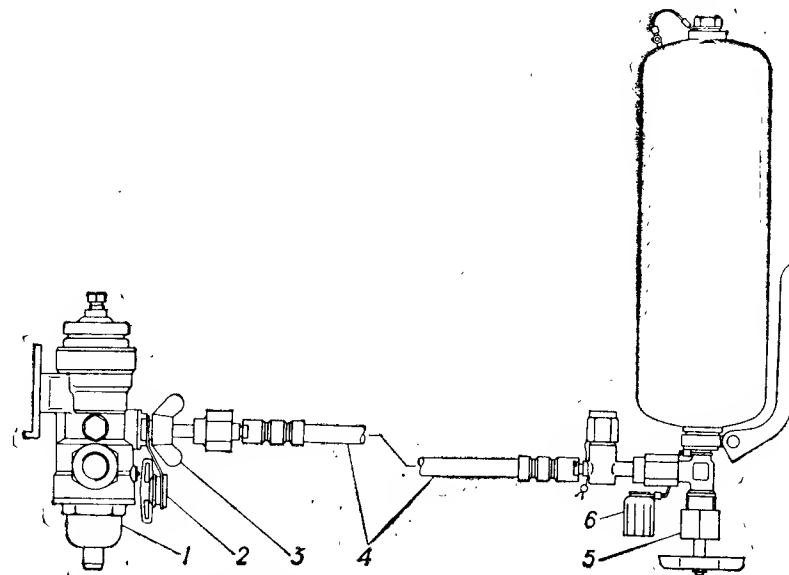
Схема снаряжения прибора ТДП сжатым воздухом:
